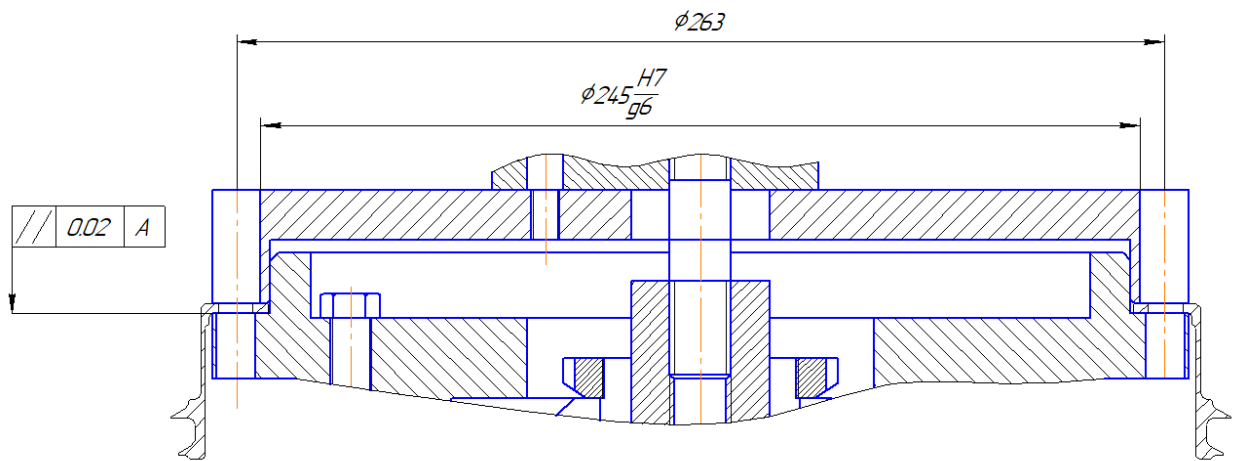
Схема встановлення деталі в пристосуванні
